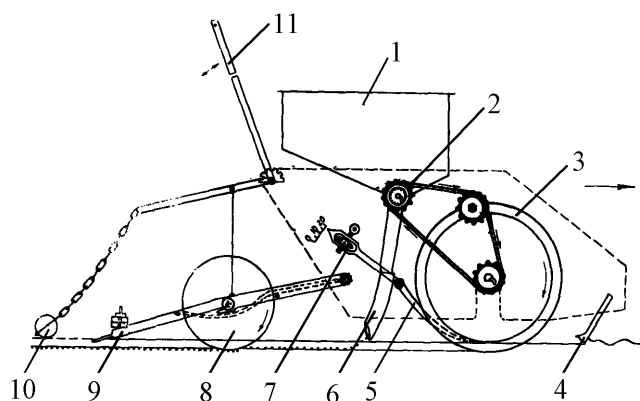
Схема сеялки «Литва-25»: 1 – бункер для семян; 2 – лопастно-ячеистый высевающий валик; 3 – бороздообразующий каток; 4 – нож-планировщик; 5 – очистительная расческа; 6 – пятиотсечный семяпровод; 7 – винтовой регулятор; 8 – вдавливающий каток; 9 – секции заделки семян; 10 – волокуша; 11 – рычаг
